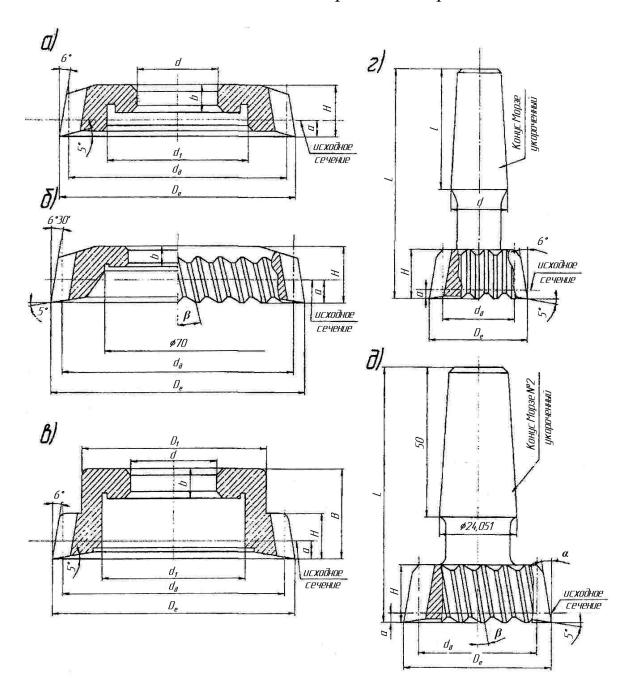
Разновидности долбяков: a — дисковый прямозубый; δ — дисковый косозубый; ϵ — чашечный прямозубый; ϵ — хвостовой косозубый
